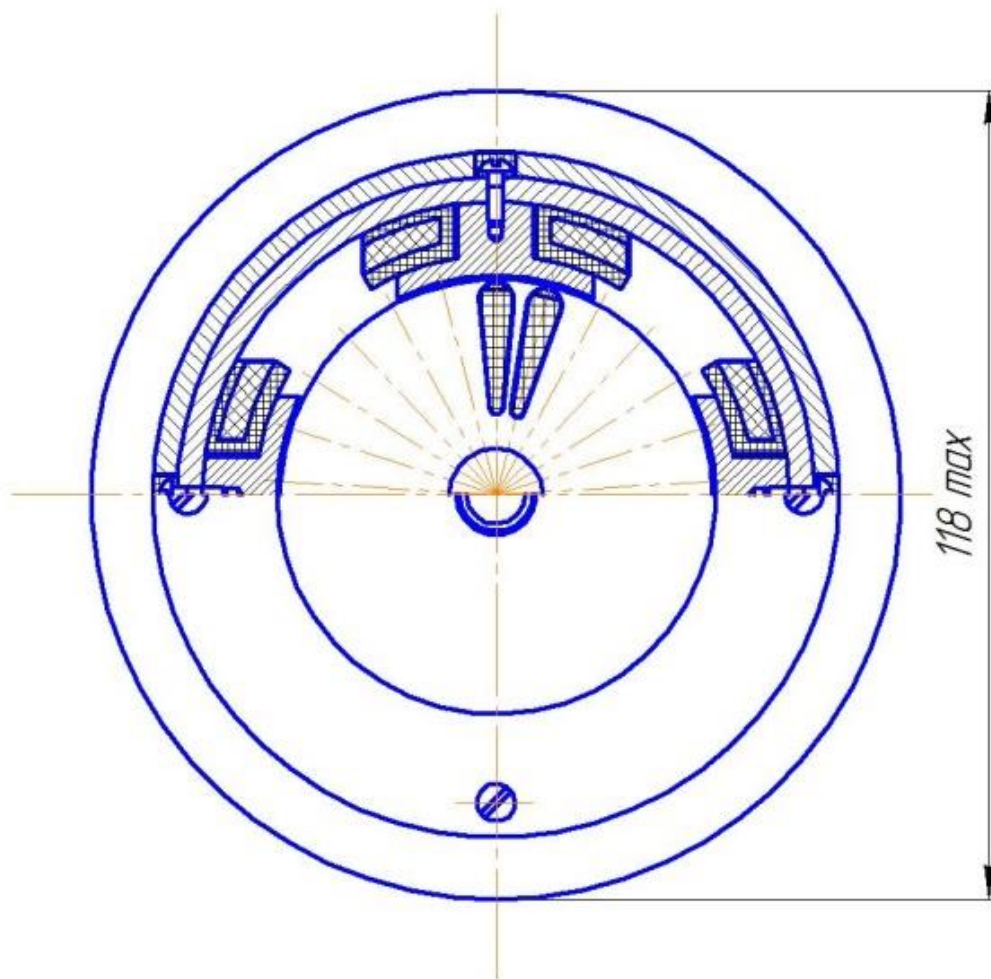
Общий вид двигателя постоянного тока (поперечный разрез)
